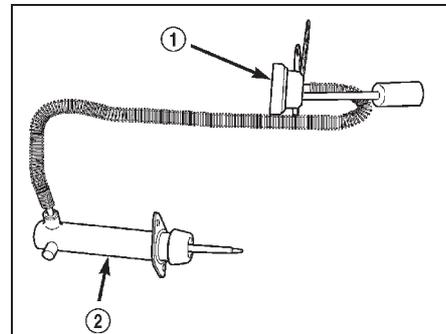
Исполнительный цилиндр сцепления. 1 - демпфер, 2 - исполнительный цилиндр.
